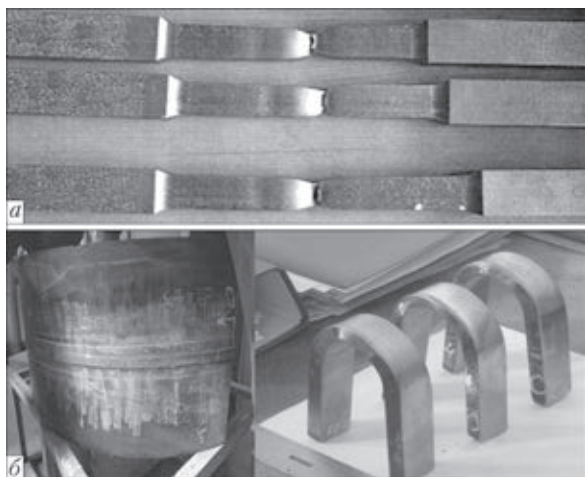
Внешний вид образцов сварных соединений труб Ду 1220×27 мм после испытаний на растяжение (а) и изгиб (б)
